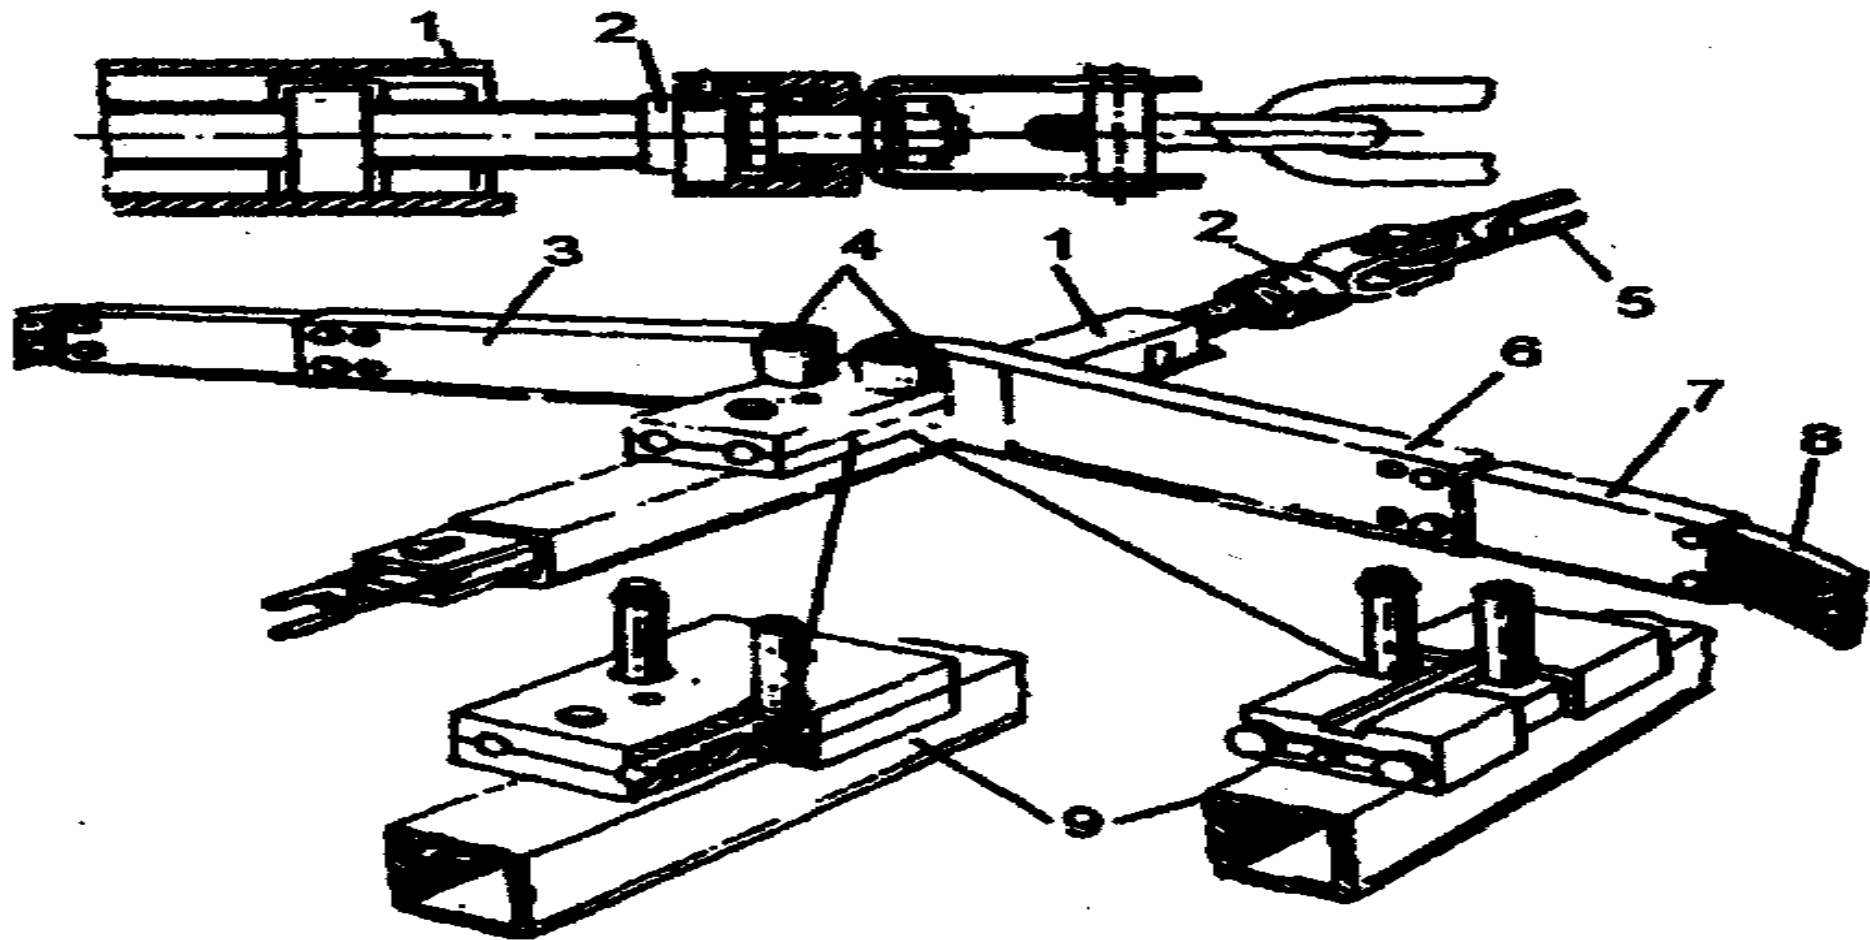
Рабочий орган скреперной установки УС-15:
